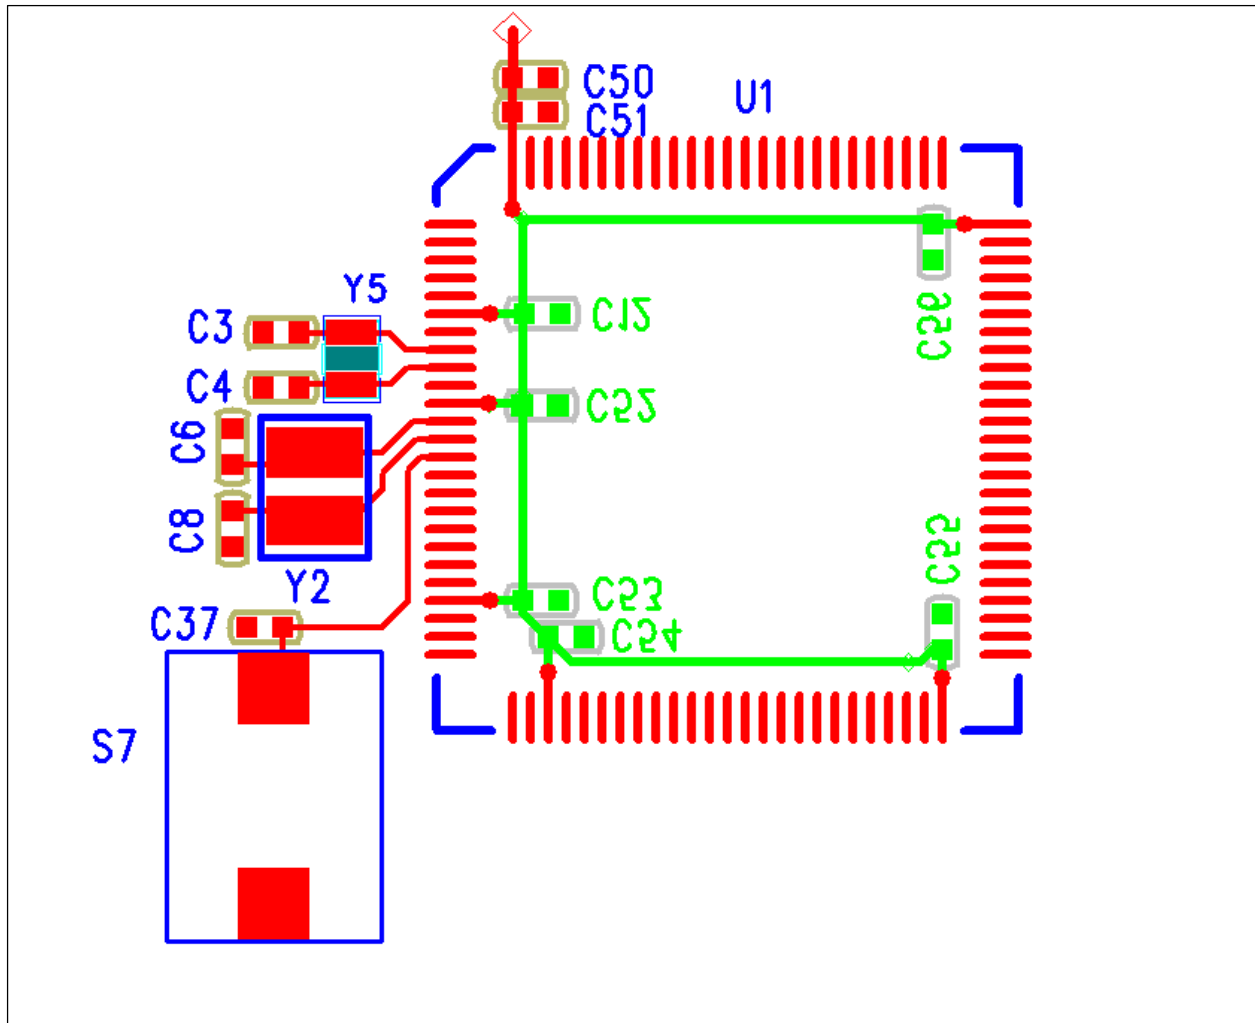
LQFP100 封装 PCB LAYOUT 参考图
